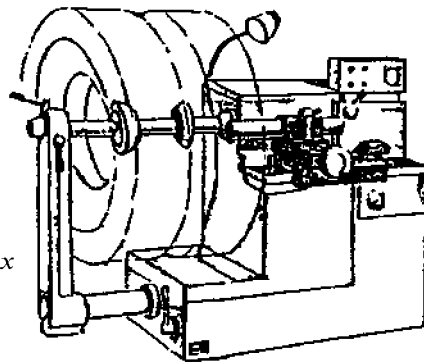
Общий вид станка Р-159 для расточки тормозных барабанов и обточки накладок тормозных колодок
